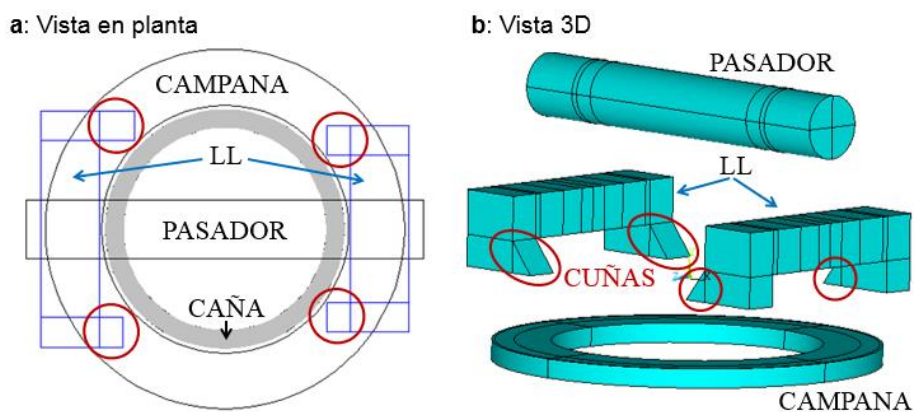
Conjunto formado por pasador-limitador-campana: (a) vista en planta y (b) vista 3D.
